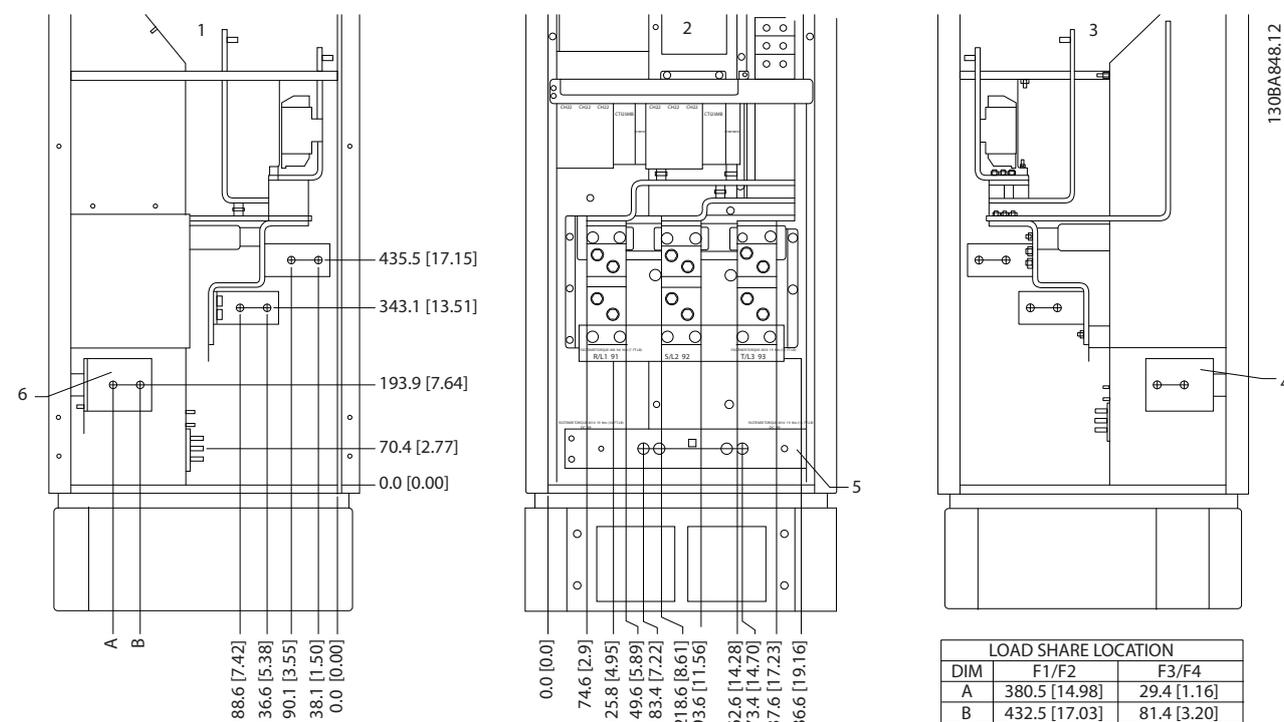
Ubicaciones del terminal: rectificador. La placa prensacables está 42 mm por debajo del nivel 0.
